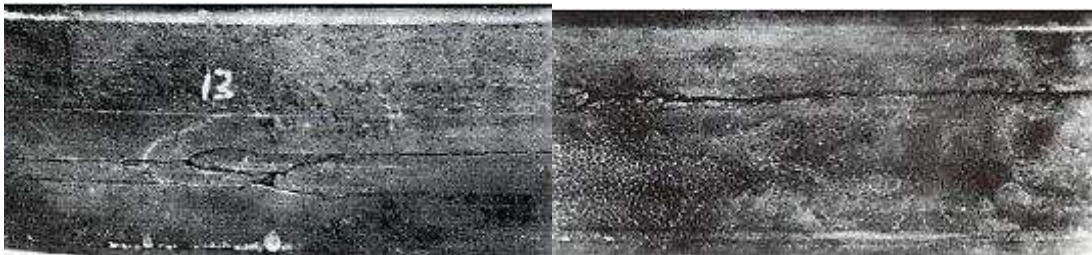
34 *Grietas y pliegues del material base debido a su proceso de fabricación.
